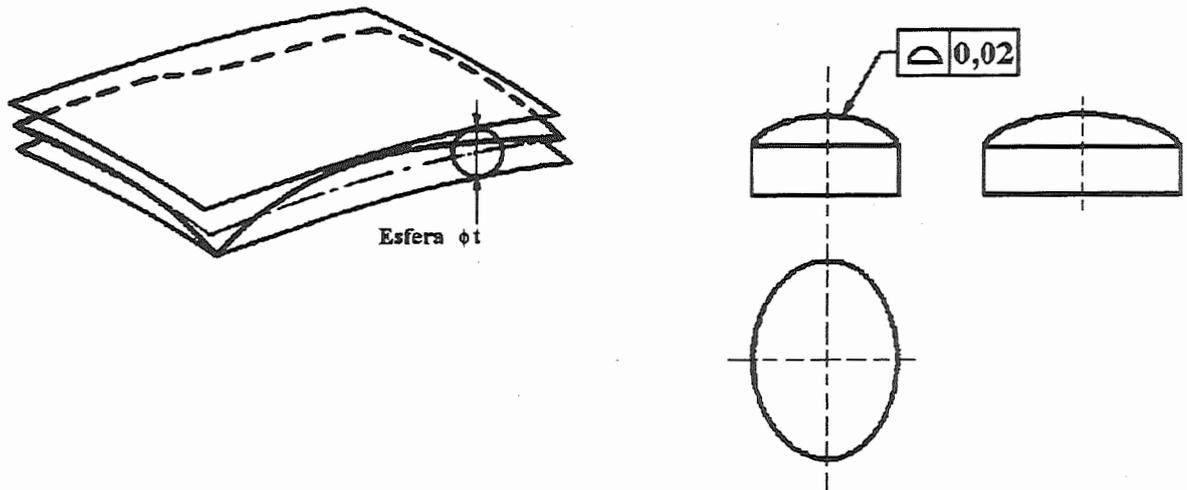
Tolerância de perfil de uma superfície qualquer
